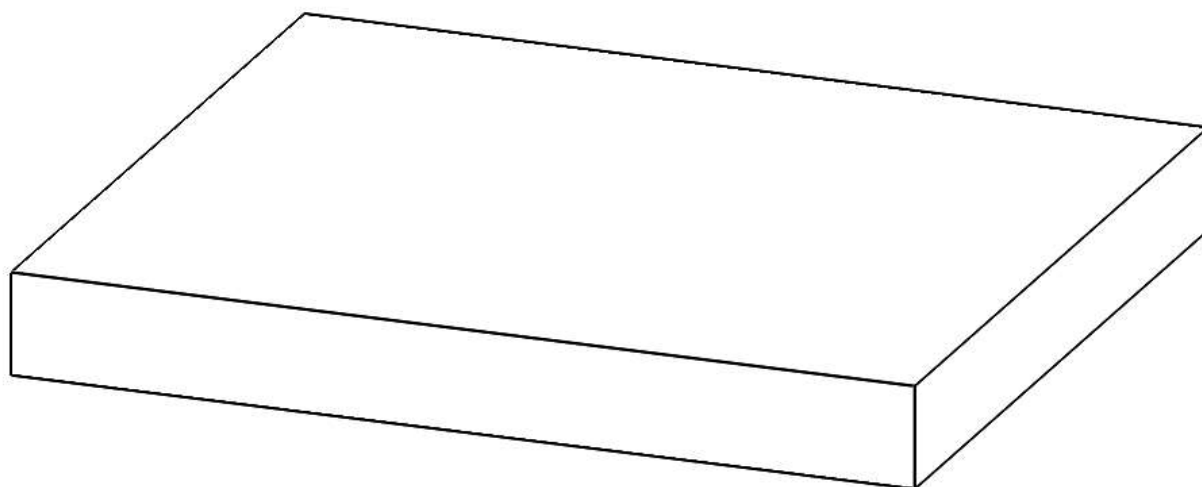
Тривимірна модель заготовки тестової деталі.
